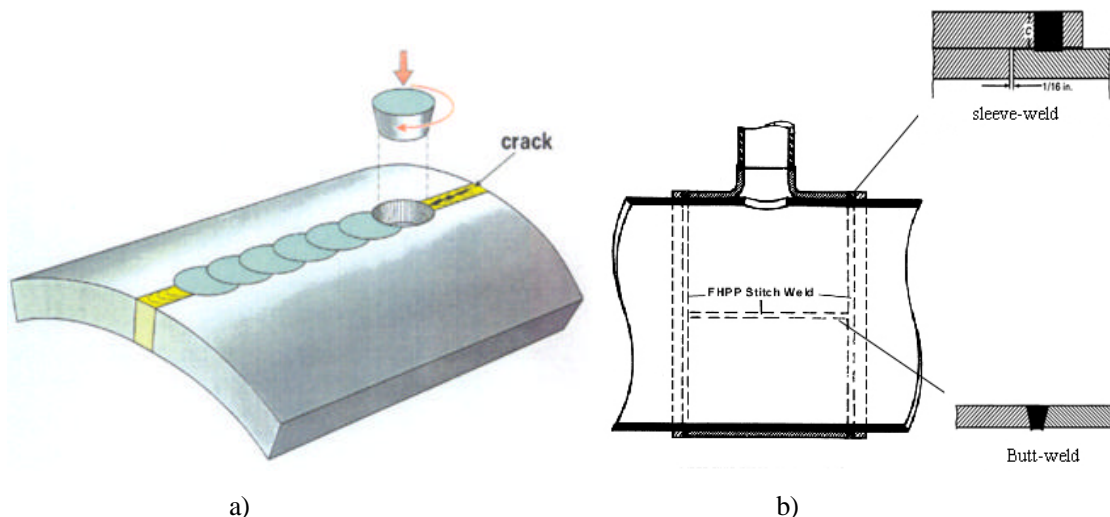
Soldagem de pinos por fricção. a) Reparo de trinca; b) instalação de calha. (www.o-vennemann.de)
